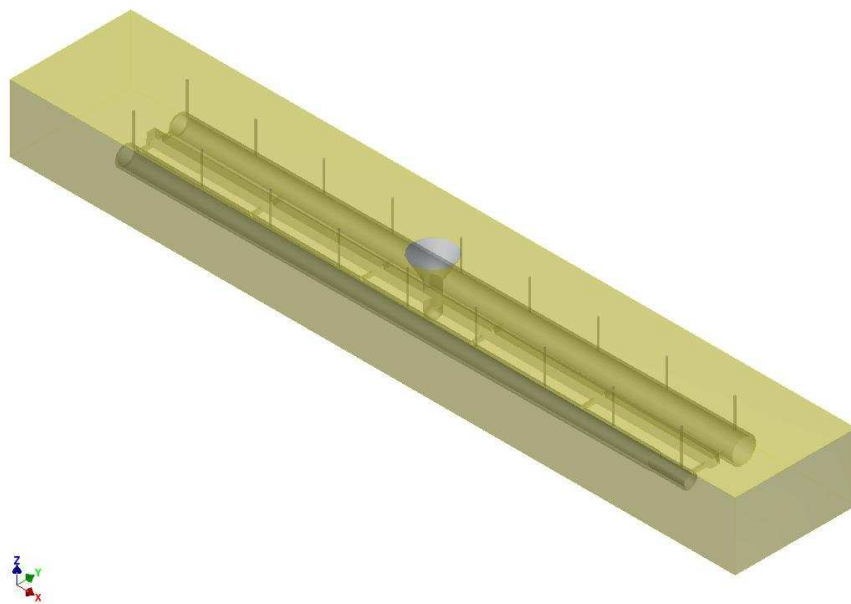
Modelo CAD de la arena de moldeo en la caja 2 de fundición.
